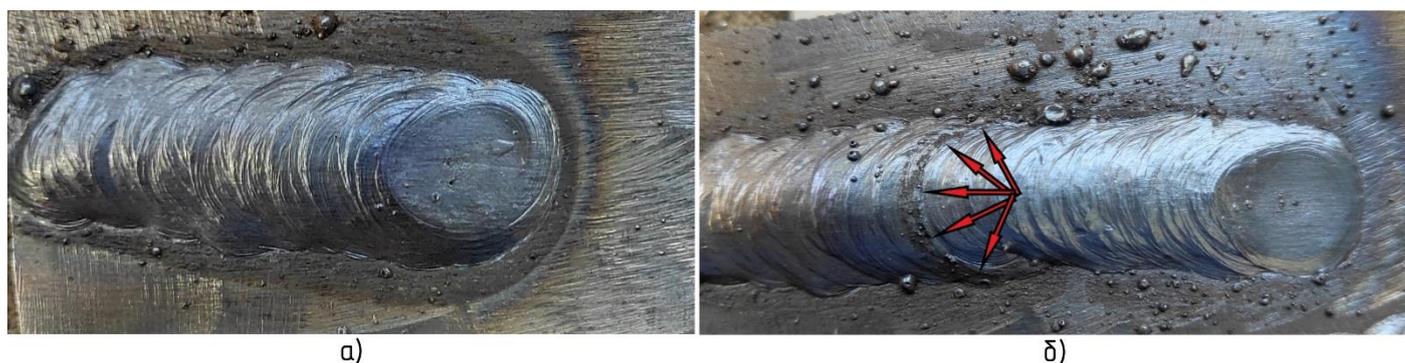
Пример бездефектного возобновления сварки в облицовочном проходе: а) место остановки; б) – стрелками указано место сплавления чешуек шва.
